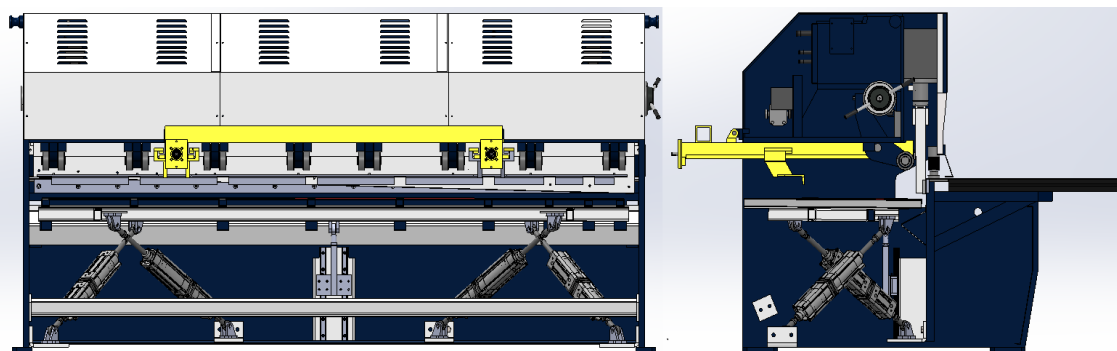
Cilindros convencionais – Posição intermédia – fase final do corte
